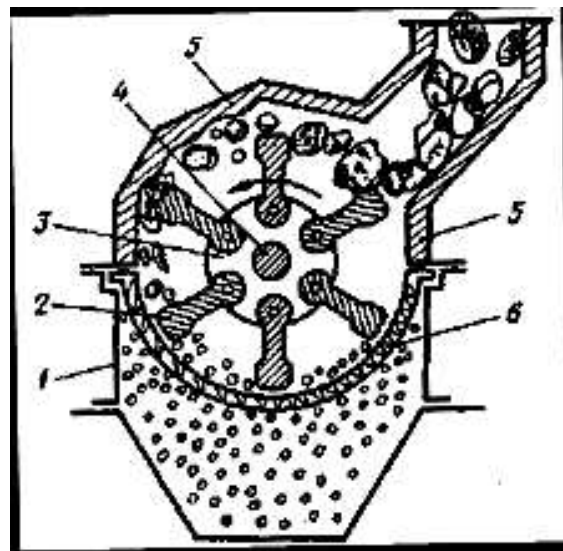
Молоткова дробарка: 1 – корпус; 2 – молоток; 3 – диск;
